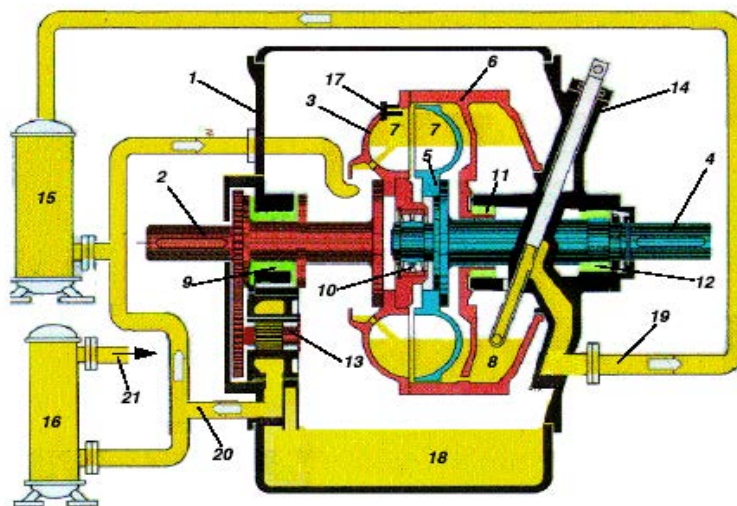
Конструкция регулировочной турбомуфты, где: 1. Корпус с масляным резервуаром; 2. Первичный вал; 3. Первичное колесо; 4. Вторичный вал; 5. Вторичное колесо; 6. Оболочка; 7. Рабочее пространство; 8. Пространство вычерпывания; 9. Осевой подшипник (подшипники 1-3); 10. Радиально-наклонный подшипник (относительный подшипник 4); 11. Подшипник 5; 12. Подшипник 6; 13. Заполняющий насос; 14. Ковшевая труба; 15. Охладитель рабочего масла; 16. Охладитель жидкой смазки; 17. Винт с плавким предохранителем; 18. Масляный резервуар; 19. Закрытая
